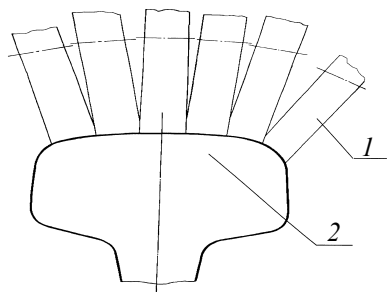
Схема установки иглофрез и лепестковых кругов на поверхности катания железнодорожного рельса:
